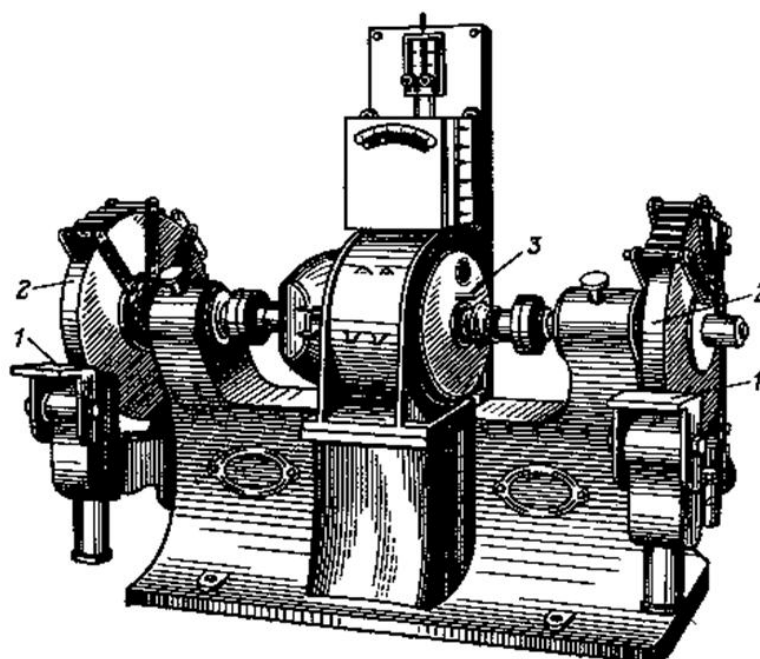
Стационарный шлифовальный станок с двумя шлифовальными кругами:
